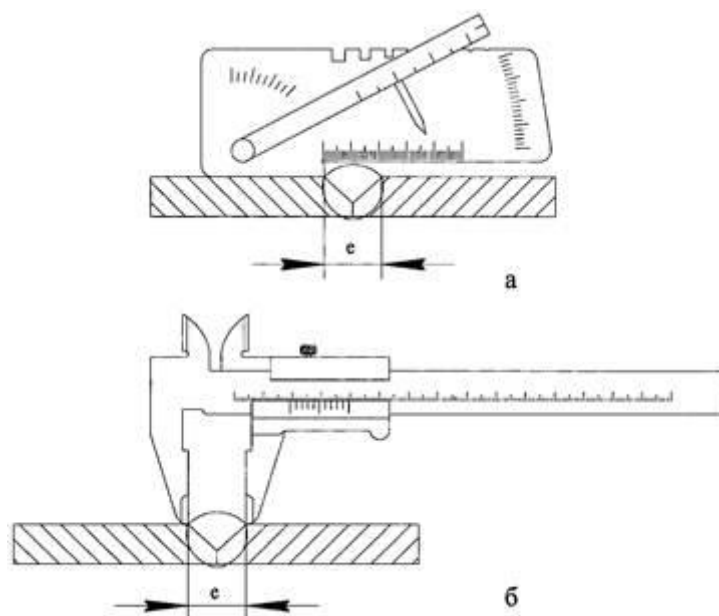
Измерения ширины шва (e) сварного соединения:
